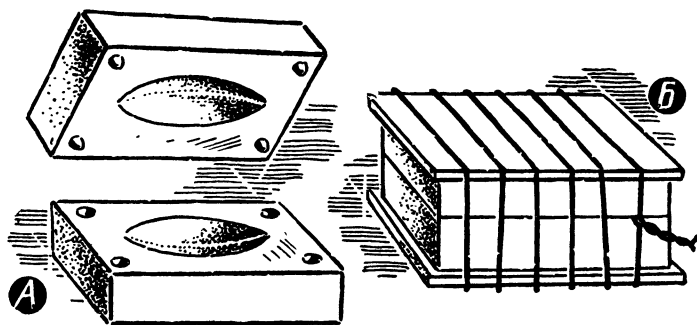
Изготовление формы: А — гипсовая форма; Б — обмотка формы проволокой.
